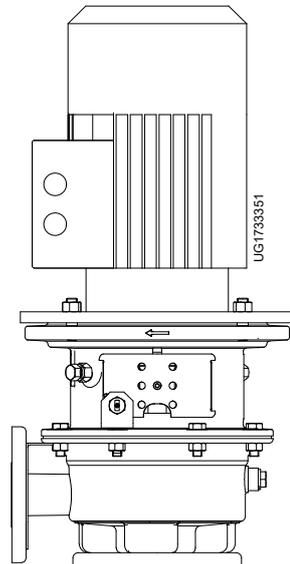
Flaschenspüler-Ausführung, Motorgröße 80 = 0,55 kW bis 180 = 22 kW
